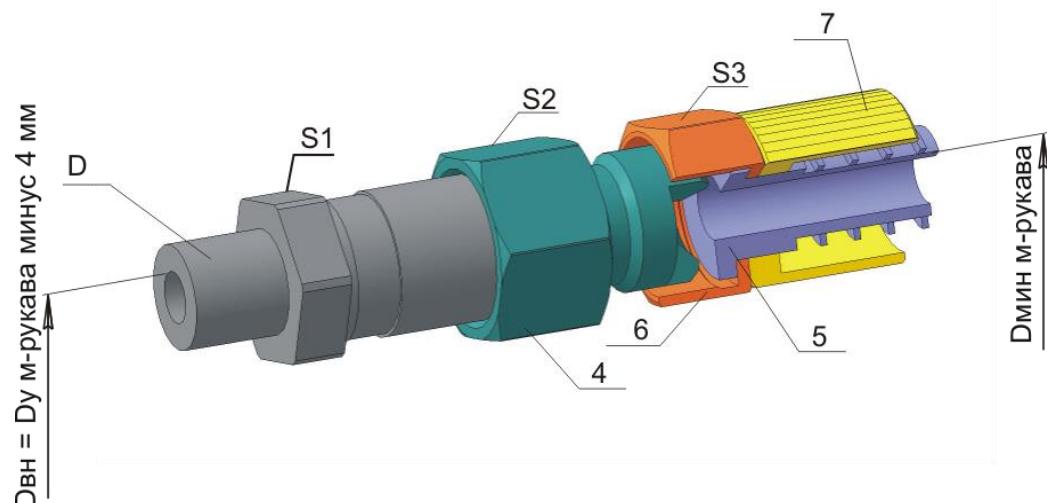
Конструкция кабельного ввода для монтажа кабеля
